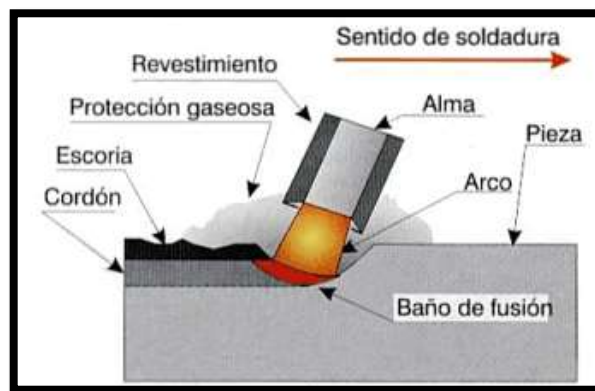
Proceso de soldadura manual con electrodo revestido (SMAW).
